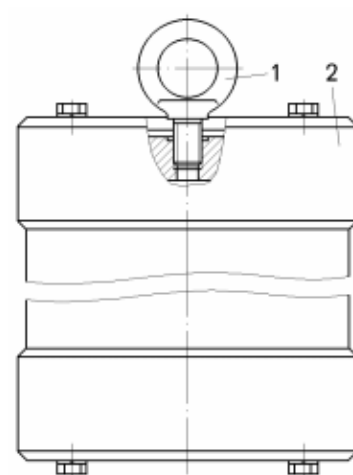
Схема зачаливания для снятия и установки пневмогидроаккумулятора:
